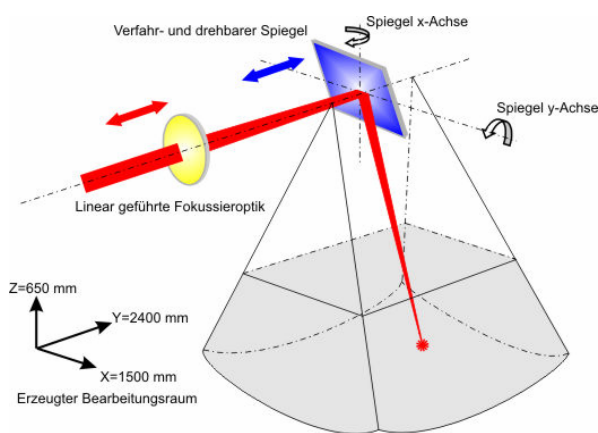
Remote-Schweißsystem (ROFIN RWS)
